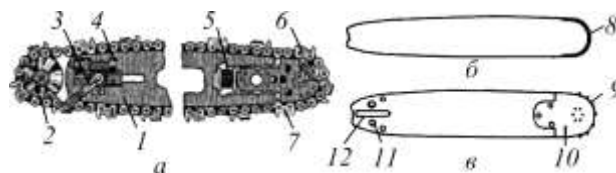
Цепной пильный аппарат моторных пил (а): 1 – пильная шина; 2 – ведущая звездочка; 3 – рукоятка; 4 – винт с гайкой; 5 – пружины; 6 – ведомая звездочка; 7 – пильная цепь; (б): - сплошные шины с концом 8, армированным твердым сплавом; (в) - направляющая шины с ведомой звездочкой: 9 – ведомая звездочка; 10 – концевая головка; 11 - отверстия под винты; 12 – прорезь для
